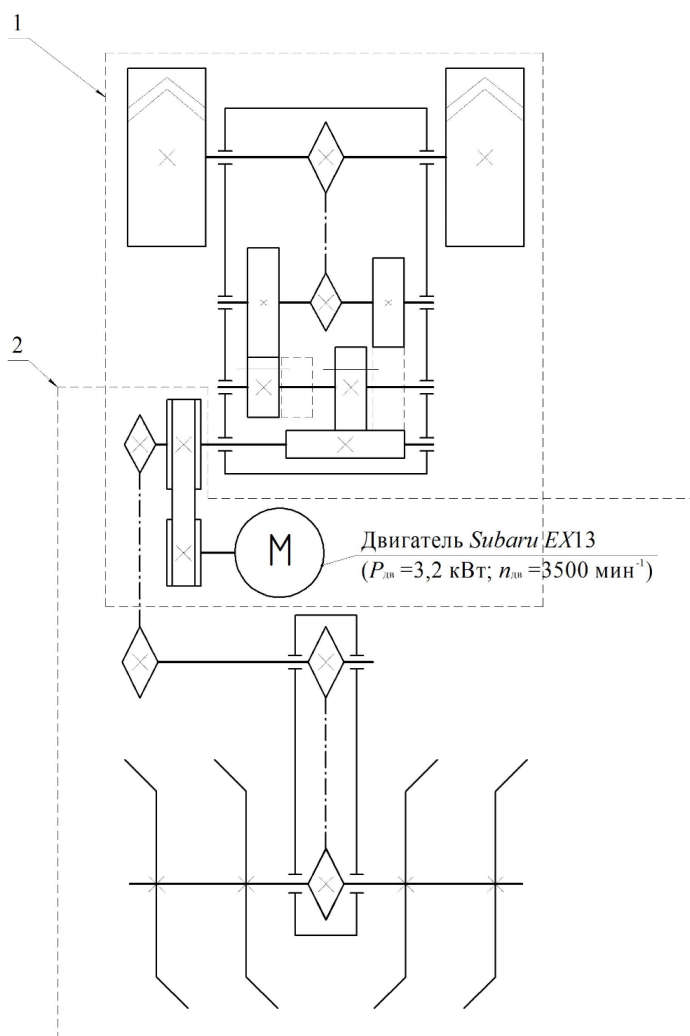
Кинематическая схема мотокультиватора МК-200 «НЕВА» со съемным фрезерным модулем
